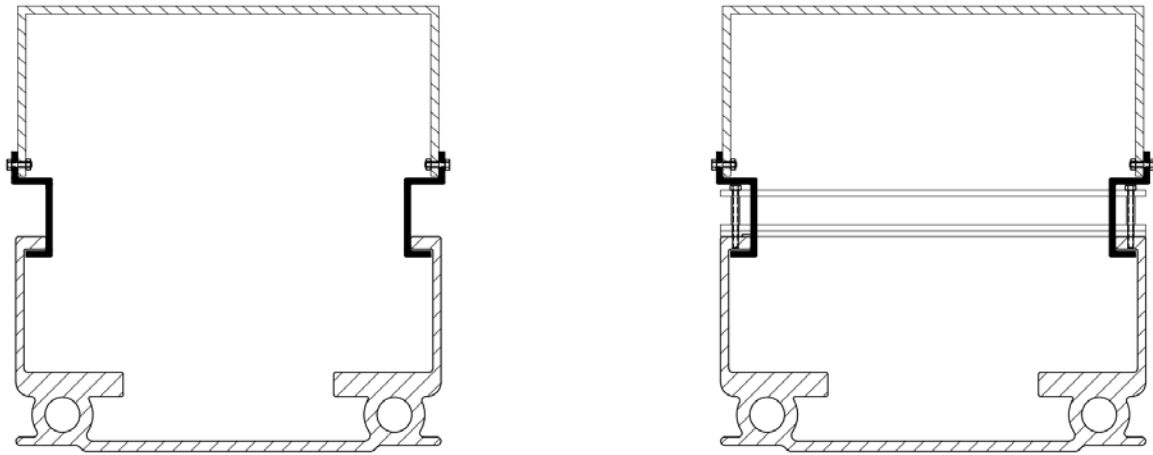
Propuesta de cubiertas de protección compatible con las placas de sujeción de cables del Minicrate.
